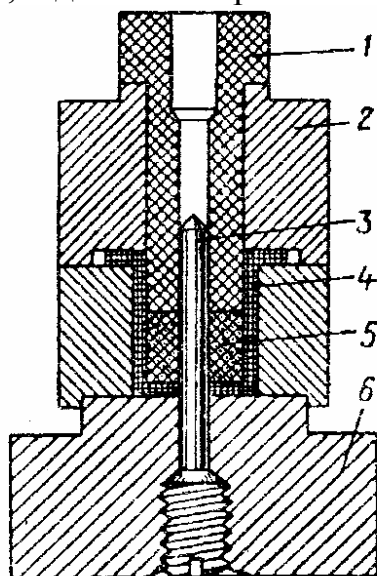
Сборка для запрессовки усилителя из ДП [87]:
